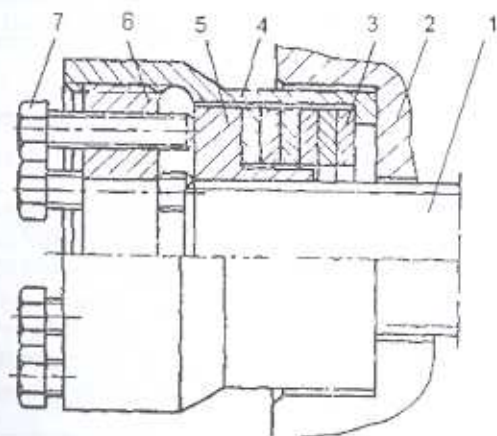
Устройство для подпрессовки активной стали статора (силовой аккумулятор [5, 6])
